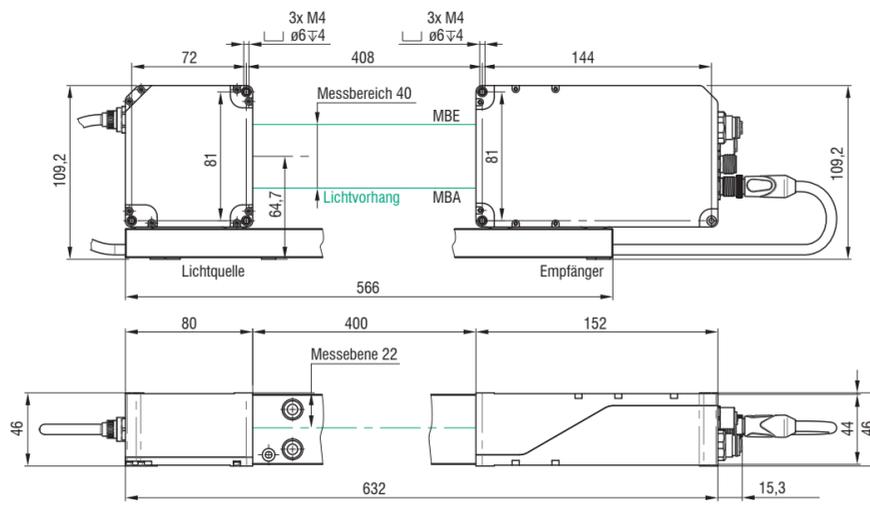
Maßzeichnung Lichtquelle und Empfänger ODC2700-40(002), Abmessungen in mm
